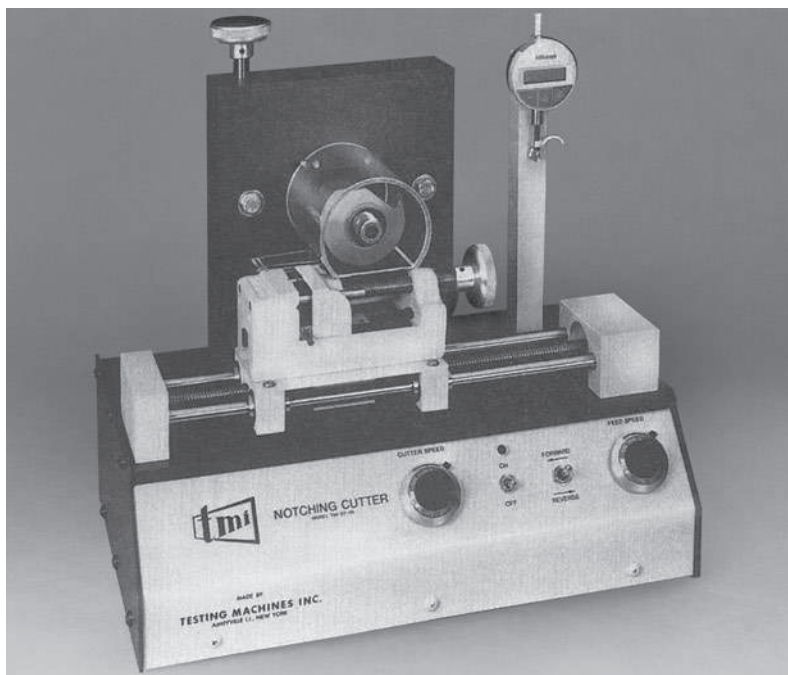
Станок для нанесения надреза на образцы, используемые при ударных испытаниях (с разрешения *Testing Machines, Inc.*)
